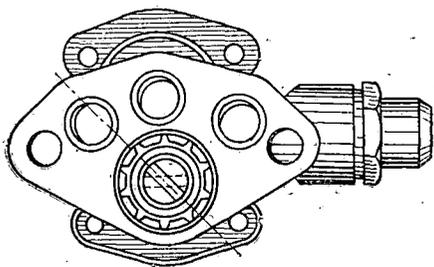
Установка масляного насоса двигателя ГАЗ-51А
